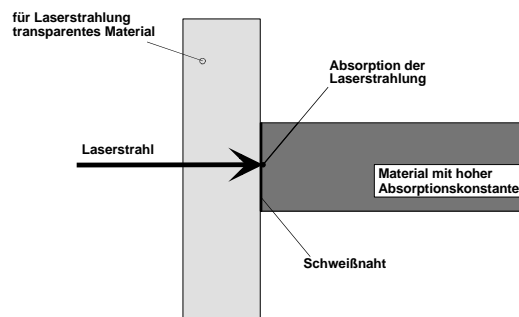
Prinzip des Durchstrahlschweißens
